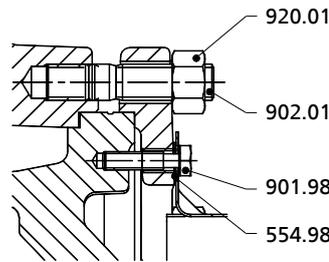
Ausführung mit geklemmtem Druckdeckel
